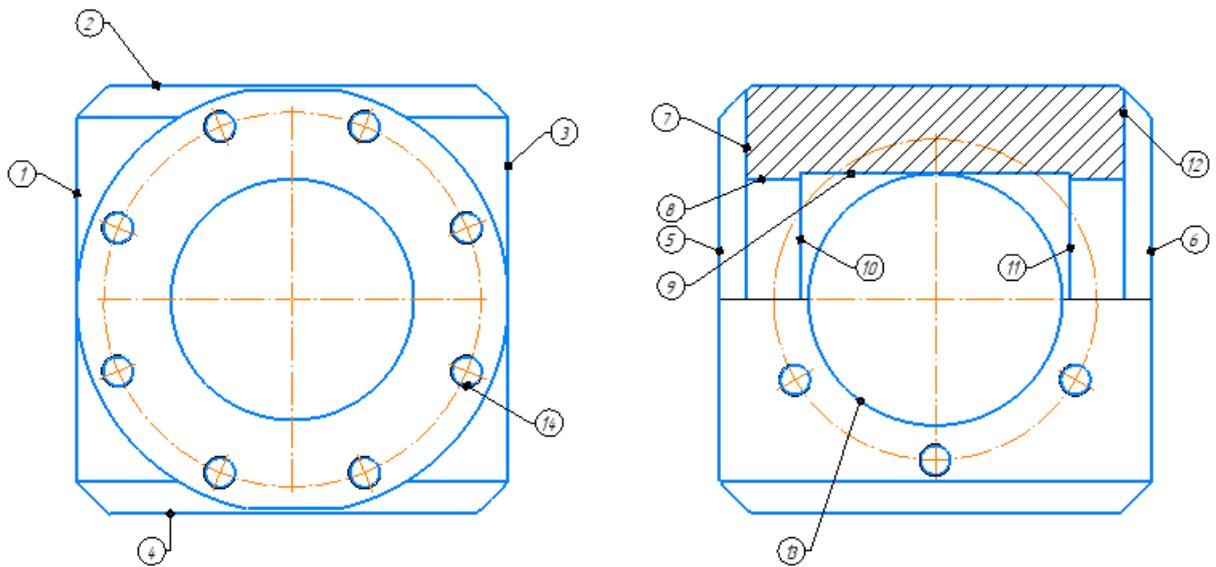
Эскиз детали с нумерацией элементарных поверхностей
